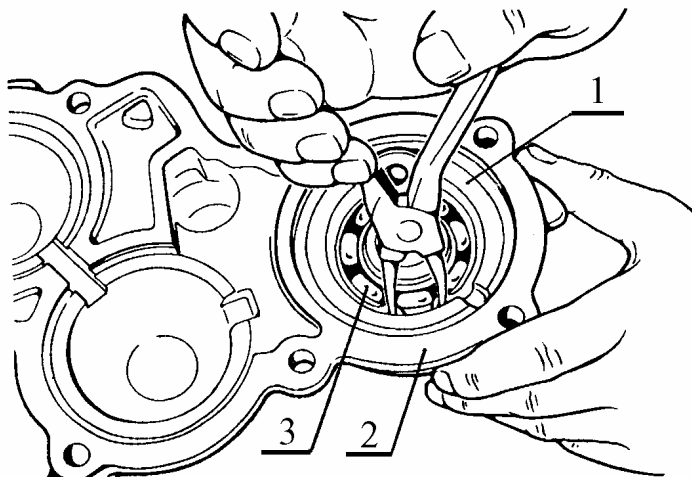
Снятие установочного кольца подшипника вала привода заднего моста:
